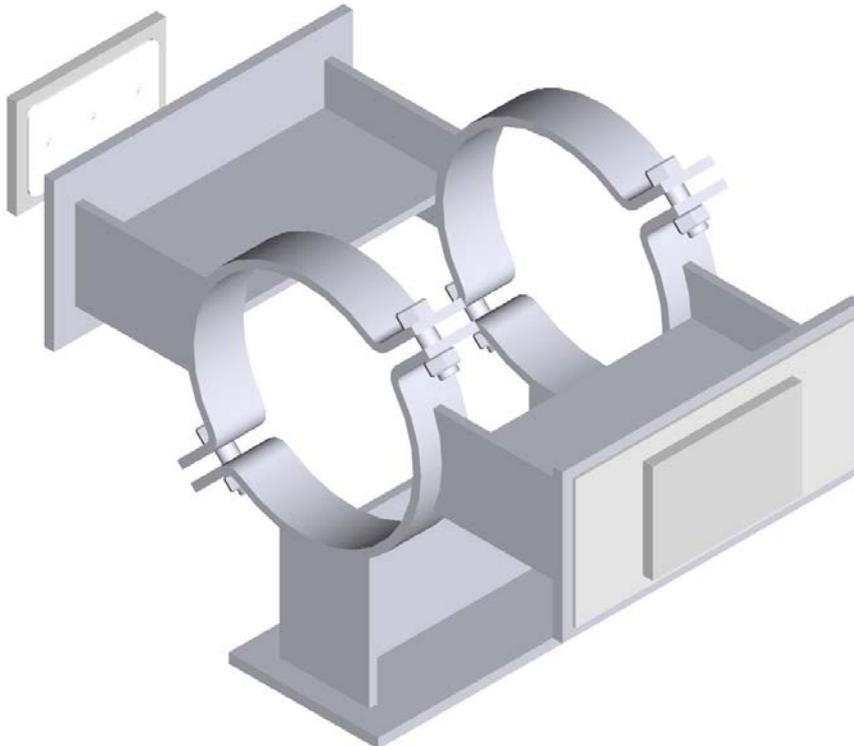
Führungslager mit 3-fach Lagerschlitten ä. SA 150H, angeschweissten Edelstahlgleitblechen (Ausführung LF) und PTFE-Gleitplatten SP 09
